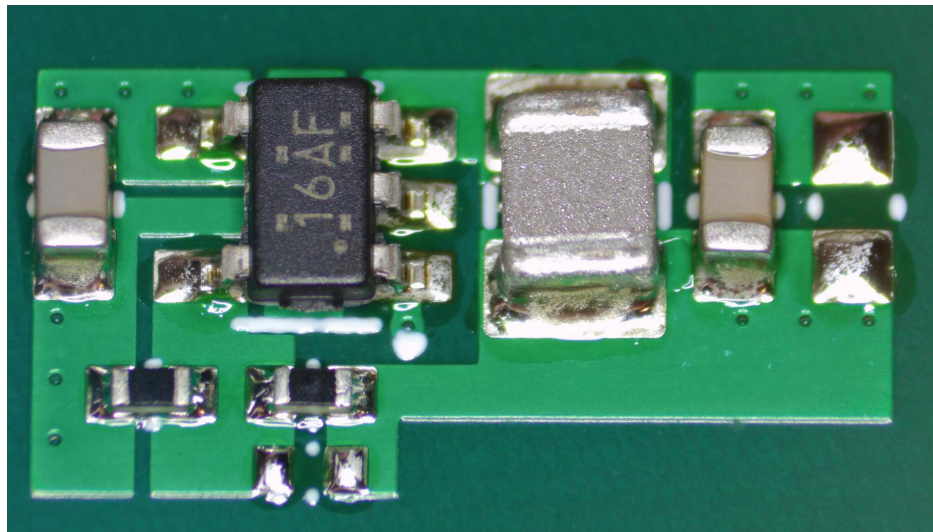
Detalle de la soldadura de uno de los reguladores.
